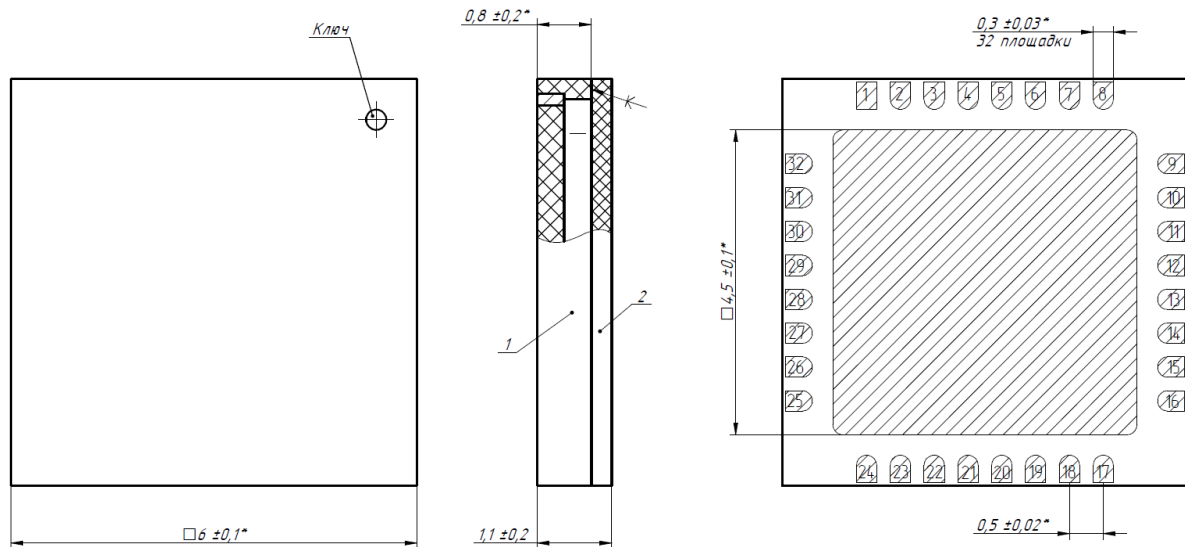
Габаритный чертёж модуля M421415-02, M421415-04
